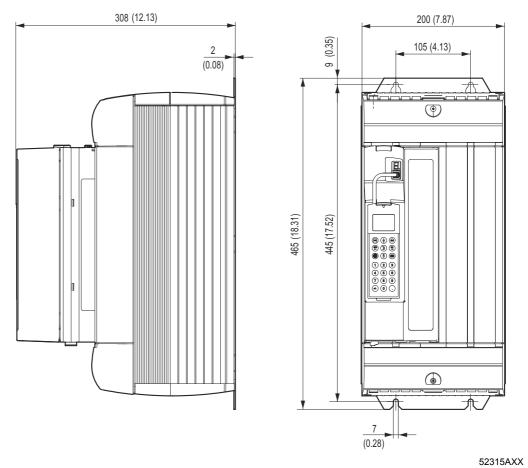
Dimensões MDX61B, tamanho 3, dimensões em mm (in)
